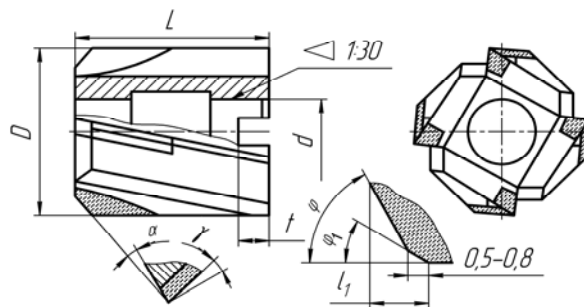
Насадной зенкер с напайными пластинками твердого сплава
